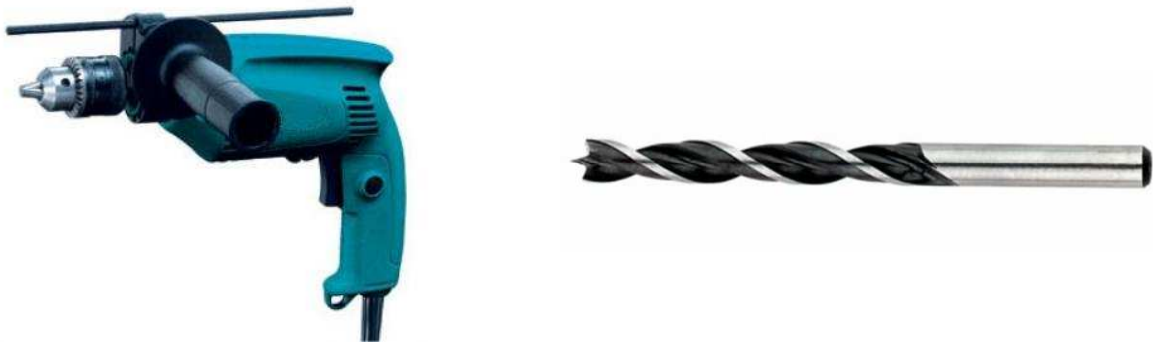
Bohrmaschine und HSS-Bohrer mit 3 Schneiden (zum Bohren von Holz)
